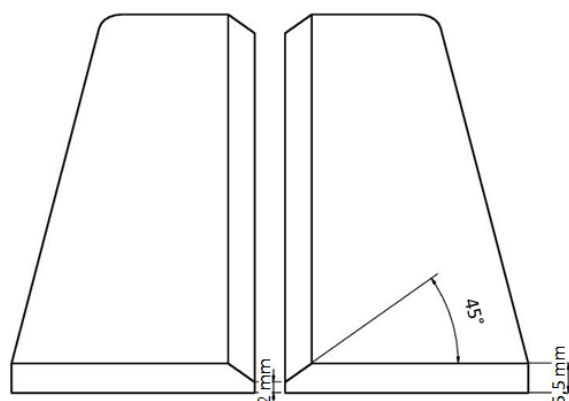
Configuração da junta de soldadura dos provetes
